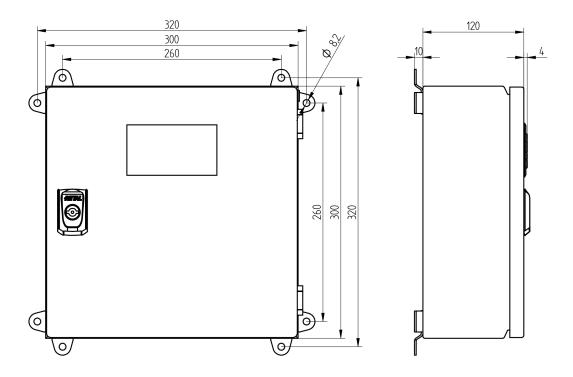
Plan coté boîtier LT4 avec supports muraux vertical/horizontal
